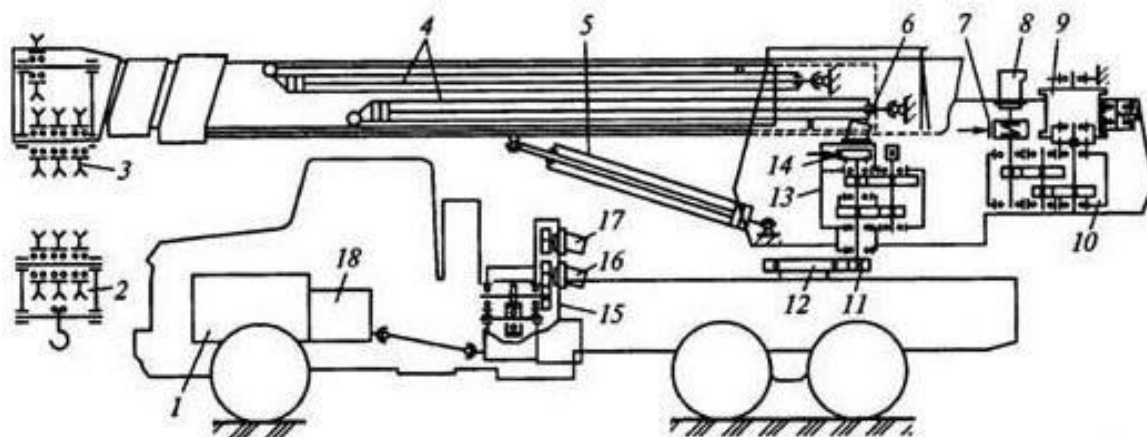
Типовая гидрокинематическая схема автокрана: 1 – дизель; 2 – крюковая подвеска; 3 – неподвижные блоки; 4 – два длинноходовых гидроцилиндра; 5 – гидроцилиндр; 6 – аксиально-поршневой гидромотор; 7 – нормально замкнутый ленточный тормоз; 8 – регулируемый аксиально-поршневой гидромотор; 9 – барабан; 10 – двухступенчатый редуктор; 11 – шестерня; 12 – зубчатый венец; 13 – двухступенчатый редуктор; 14 – нормально замкнутый колодочный тормоз; 15 – раздаточная коробка; 16, 17 – аксиально-поршневые гидромоторы; 18 – коробка передач.
